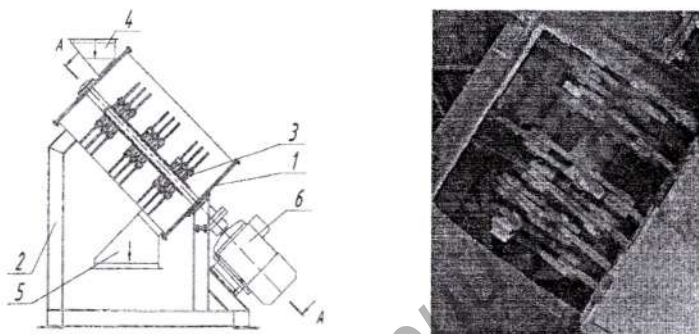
Схема и общий вид молотковой дробилки с наклонным корпусом
